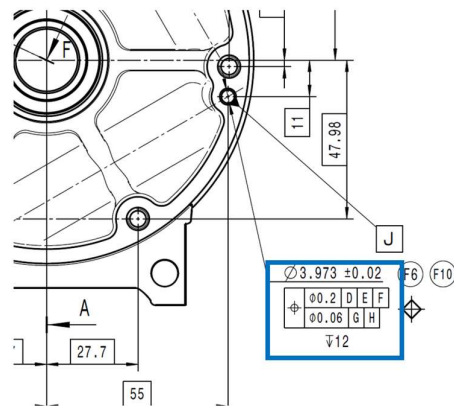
Datum G com furos com tolerâncias de posição dependentes da face de encosto (datum D) e dos furos (datum E-F)
